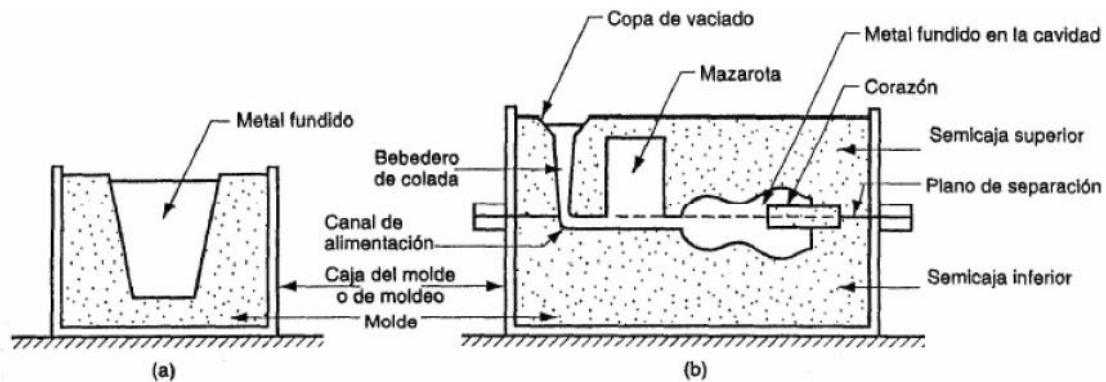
Esquema de una fundición y sus partes, (a) Molde abierto, (b) Molde cerrado. [10]
